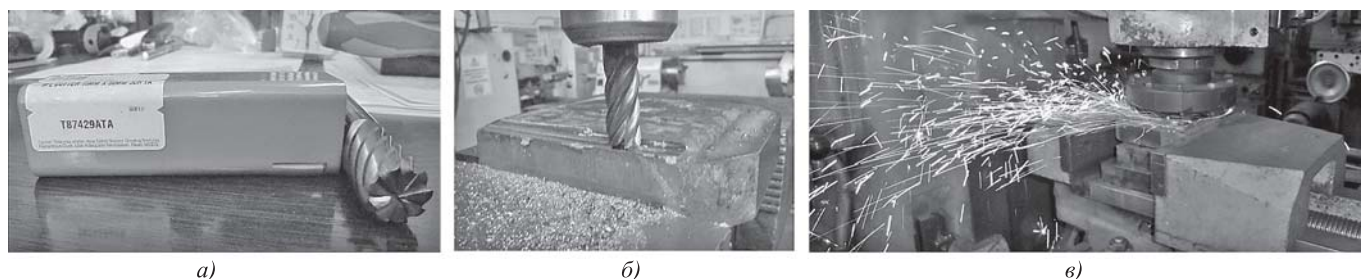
Примеры используемых фрез (а), фрезерования наплавки фрезой монолитной концевой (б) (диаметр 15 мм, 9 зубьев, скорость резания 75 м/мин, подача 65 мм/мин, глубина фрезерования 0,75 мм, ширина фрезерования 8 мм) и торцевой фрезой (в)
